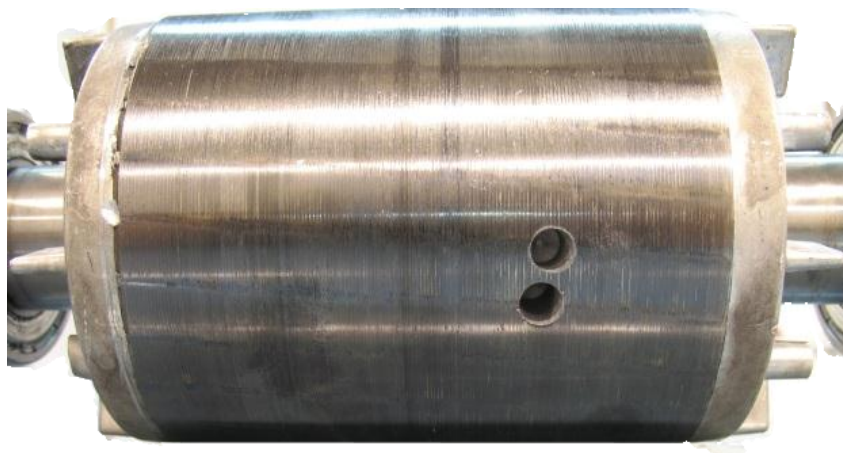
Rotor utilizado en el ensayo de barras fracturadas
